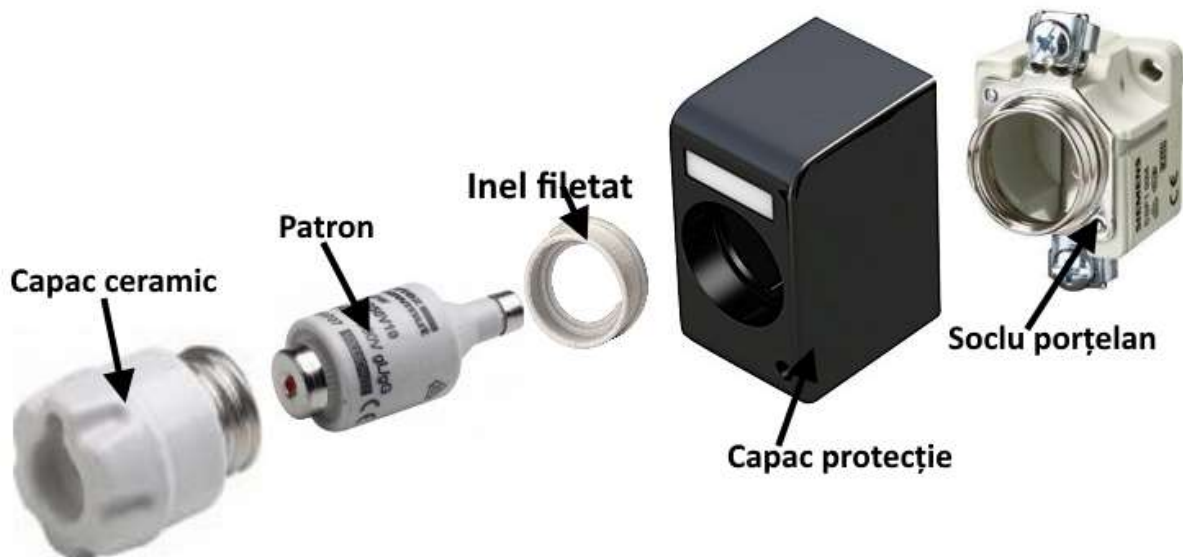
Elemente constructive siguranță fuzibilă cu filet
